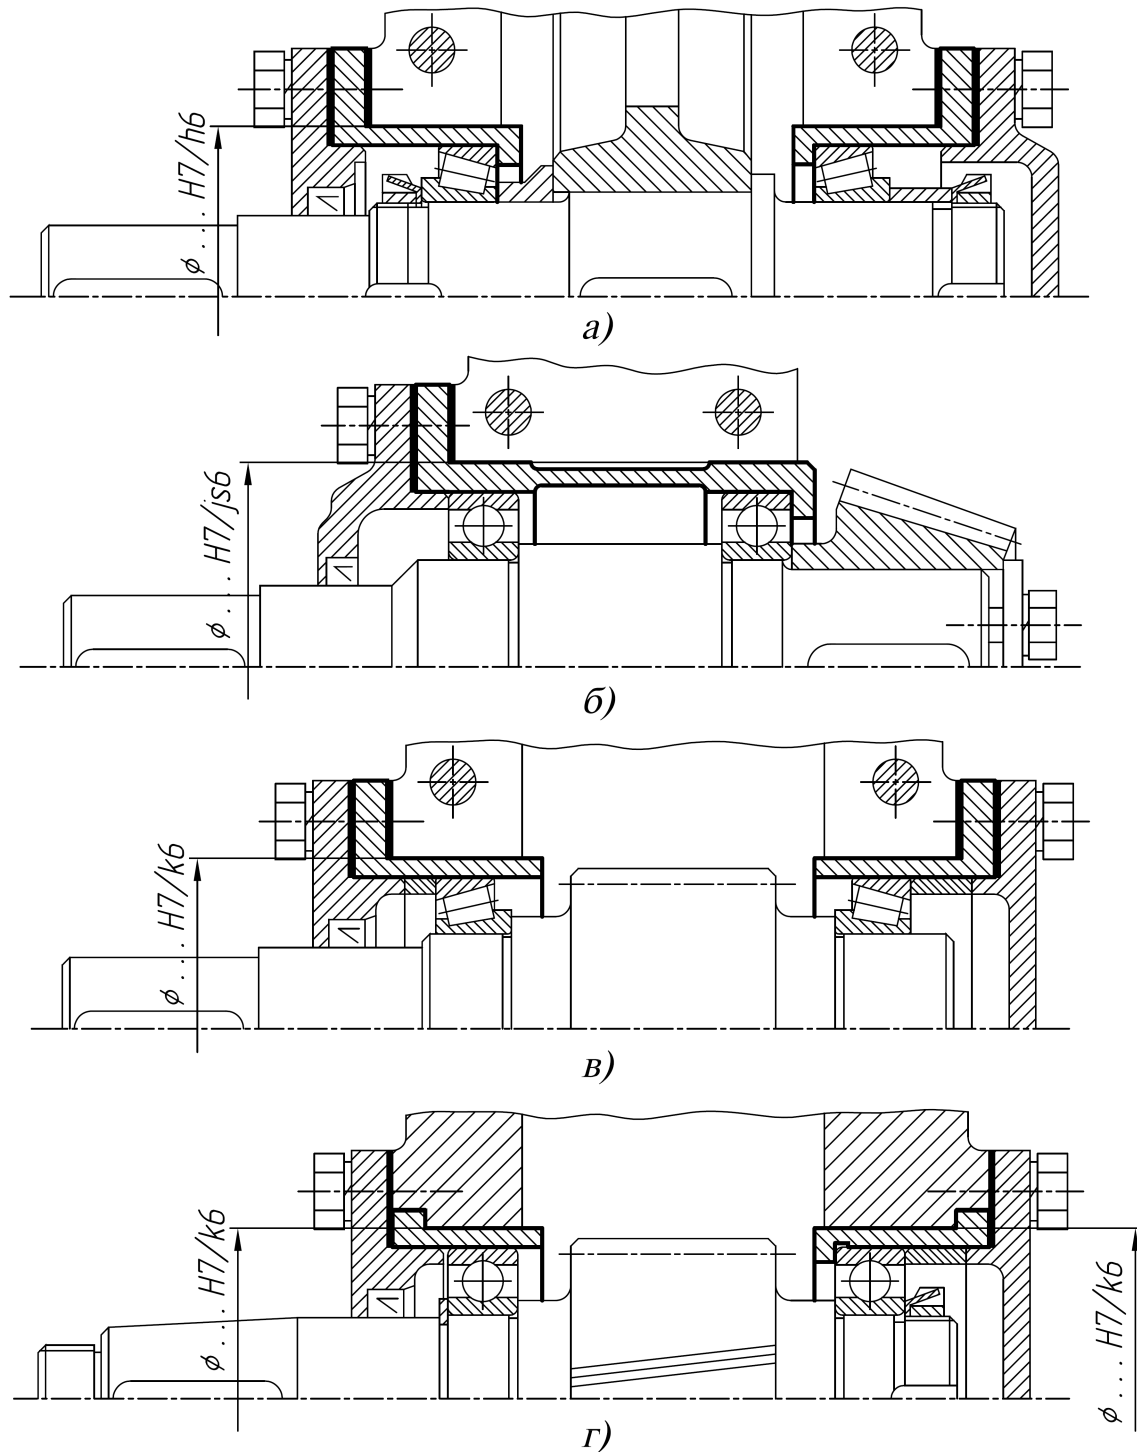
Приклади установки стаканів: а – вал циліндричної передачі; б – вал конічної передачі; в – черв'ячний вал черв'ячної передачі; г – вал-шестерня циліндричної косозубої передачі
